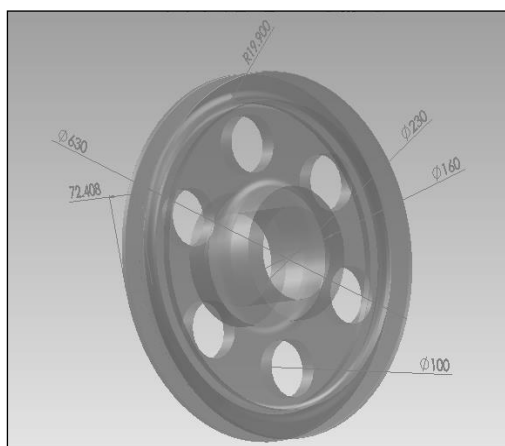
Geometrie CAD și dimensiuni rolă inițială.
